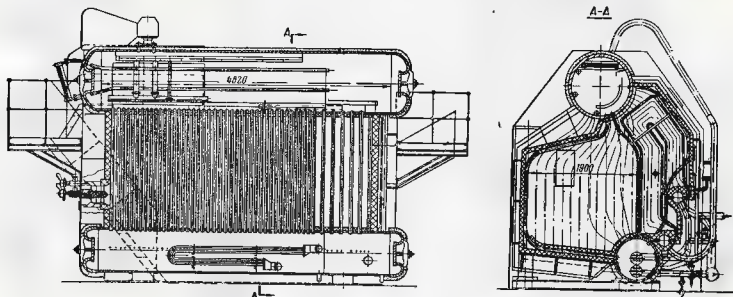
Газомазутный паровой котел типа ГМ-10-39
